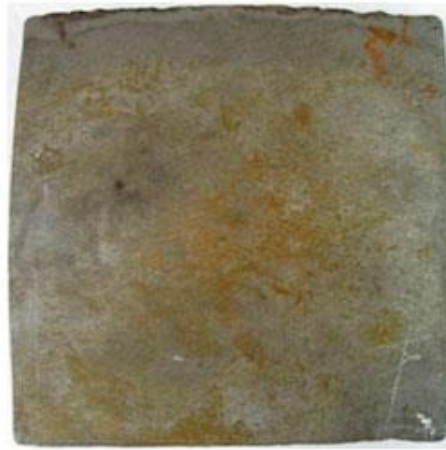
Поперечное сечение сортовой заготовки с выпученными боковыми гранями
